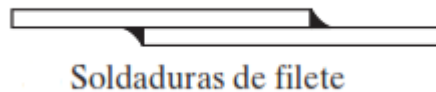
Soldadura a Filete (McCormac & Csernak, 2012)
